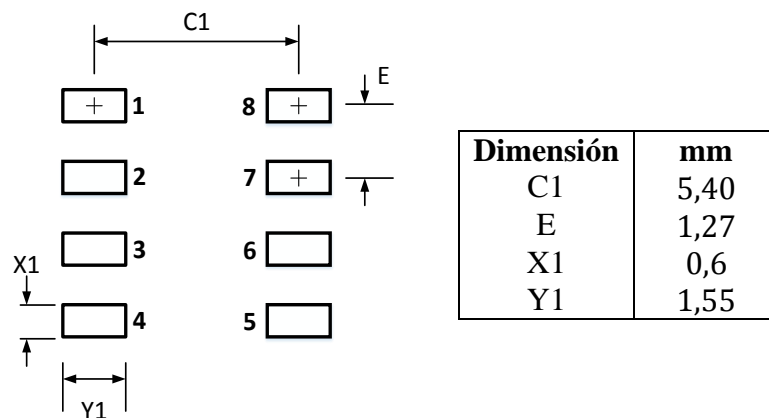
Dimensiones para el optoacoplador en el PCB
